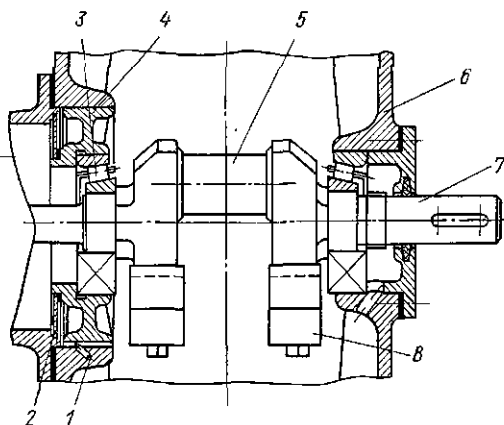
Двухопорный коленчатый вал на конических подшипниках:
